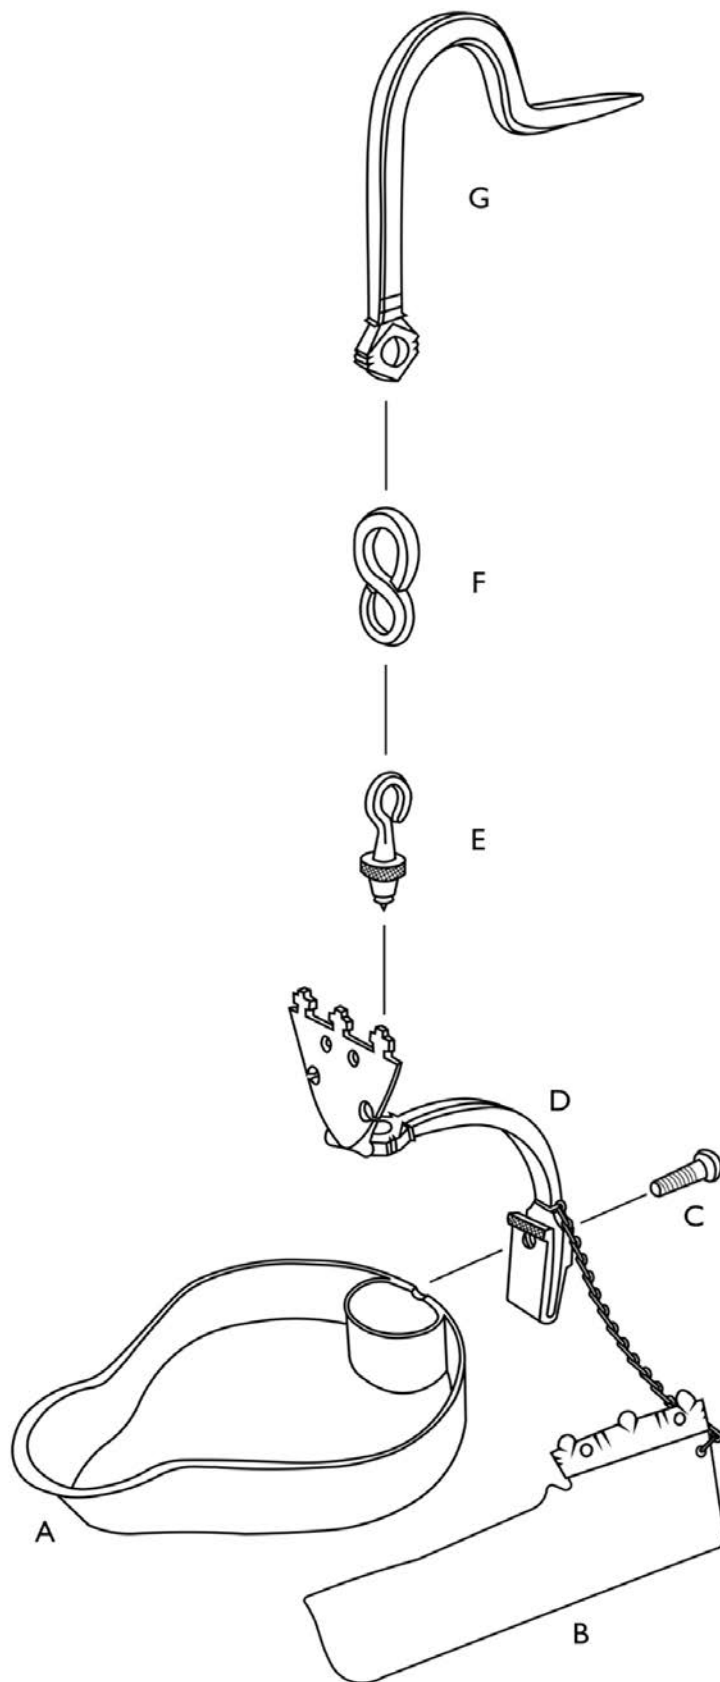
Idealisierte Explosionszeichnung einer Harzer Unschlittlampe mit Kreuzschild nach einem Original aus der Zeit um 1800 und Bezeichnung der einzelnen Bestandteile: A – Lampenschale; B – Dochtblech mit Befestigungskette; C – Bügelschraube; D – Bügel mit Schild; E – Wirbel mit Drehlager (stilisierte Eichel); F – Zwischenglied; G – Haken. (Grafik © Jan Büttner)
